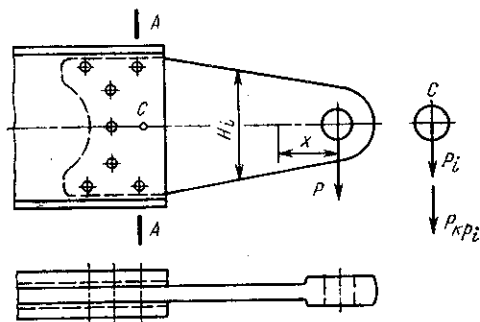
Кронштейн, устанавливаемый на стенке
